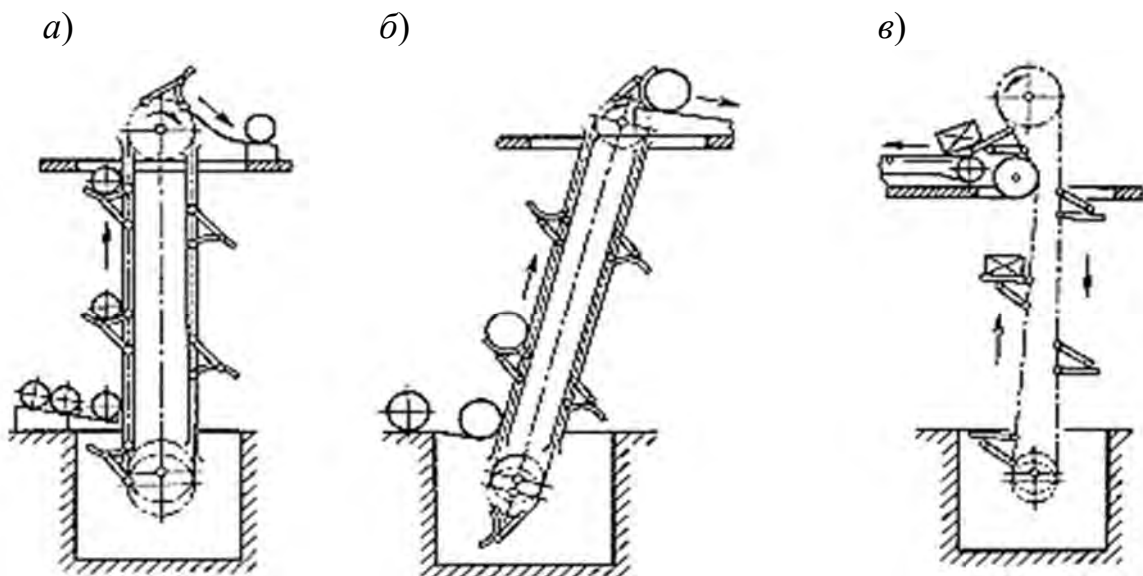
Схемы и способы загрузки и разгрузки полочных элеваторов: а – вертикальный; б – наклонный; в – вертикальный с отклонением захвата на рабочей ветви
